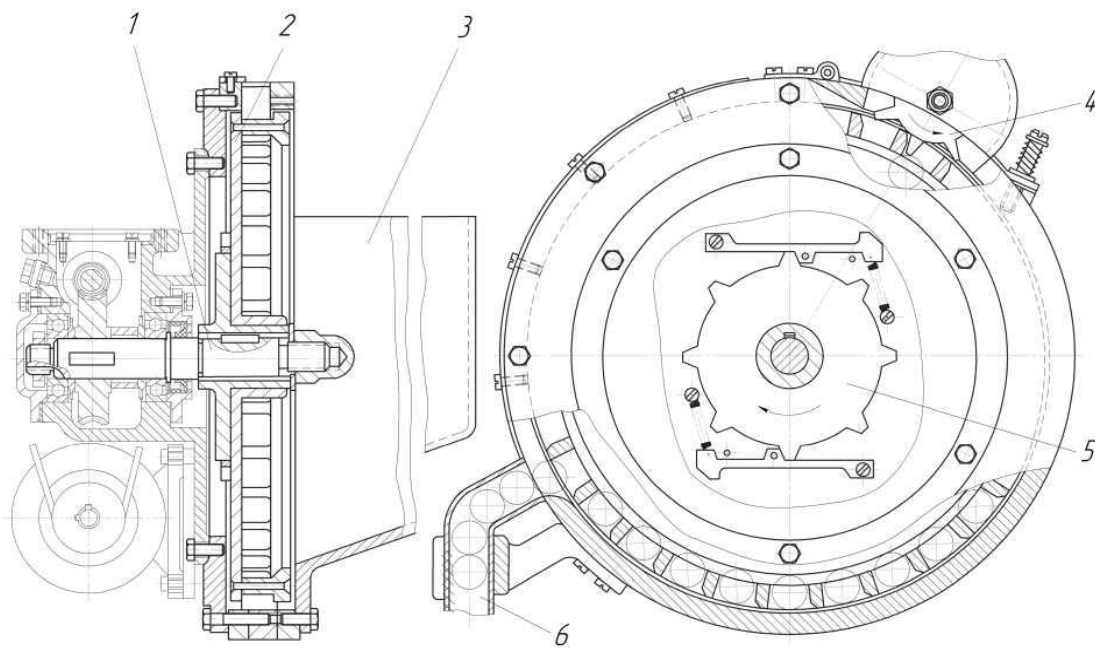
Механічний дисковий вертикальний комірковий бункерний завантажувальний пристрій для металевих і пластмасових ковпачків, що закручуються: 1 – вал; 2 – диск; 3 – бункер; 4 – зірочка для виштовхування неправильно орієнтованих та застряглих ковпачків; 6 – приймач
